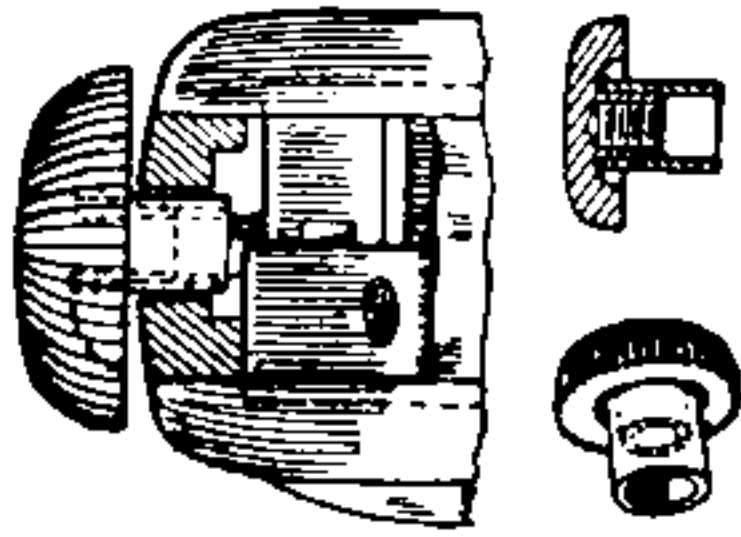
Collare montato sul bottone di carica per eliminare il giuoco.
